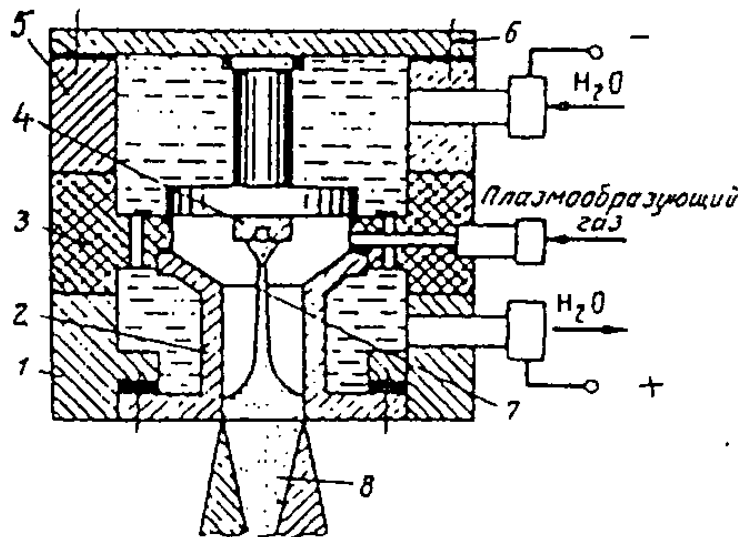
Конструктивная схема плазменного распылителя
